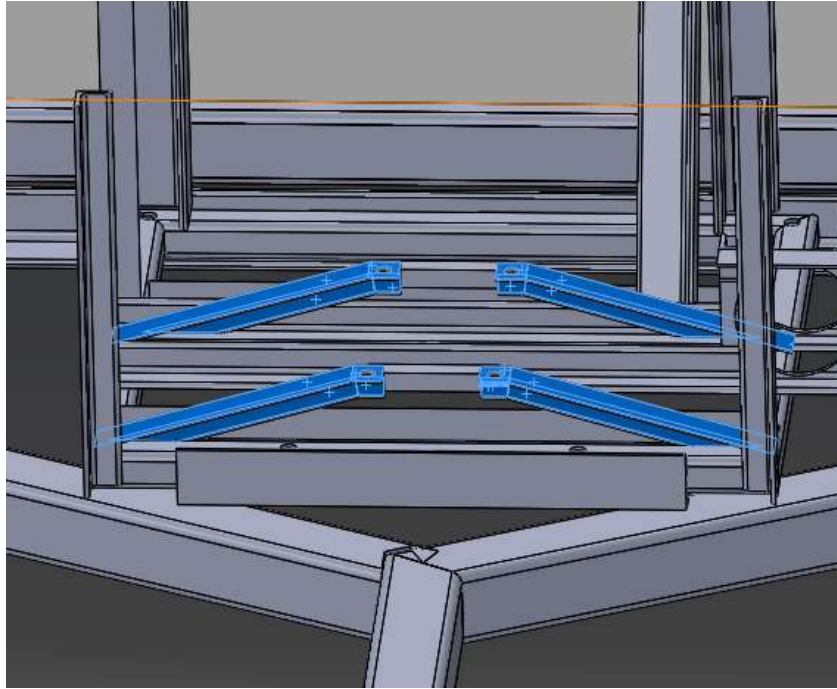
Destaque das cantoneiras de apoio para as chumaceiras
